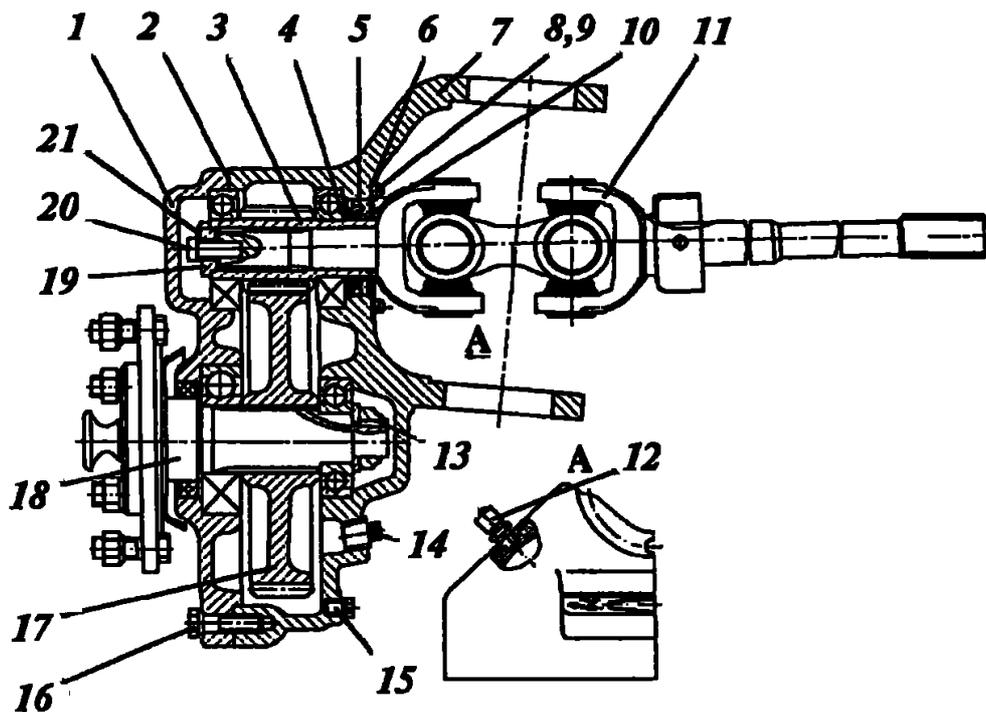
Редуктор: 1 - крышка; 2 - прокладка; 3, 17 - шестерни; 4 - подшипник; 5 - манжета; 6 - кольцо; 7 - корпус; 8 - винт; 9, 19 - шайбы; 10 - грязевик; 11 - шарнир; 12 - сапун; 13 - гайка; 14, 15 - пробки; 16, 20 - болты; 18 - фланец; 21 - пластина фиксирующая
